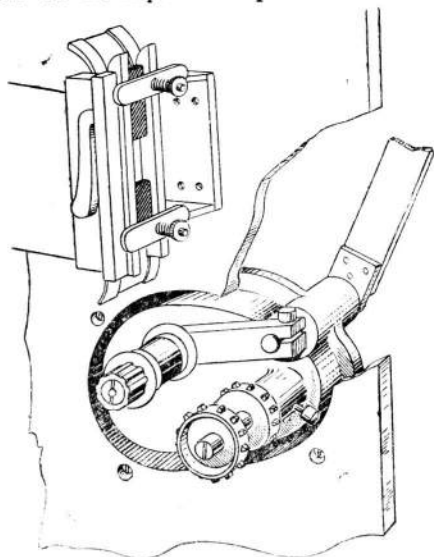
Крепление ролика установки кадра в рамку на коробке мальтийского механизма
